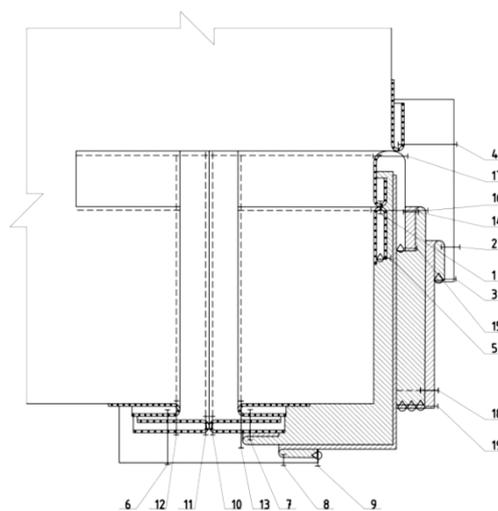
Сборочный чертеж прорезного кармана с двумя накладываемыми линиями входа
